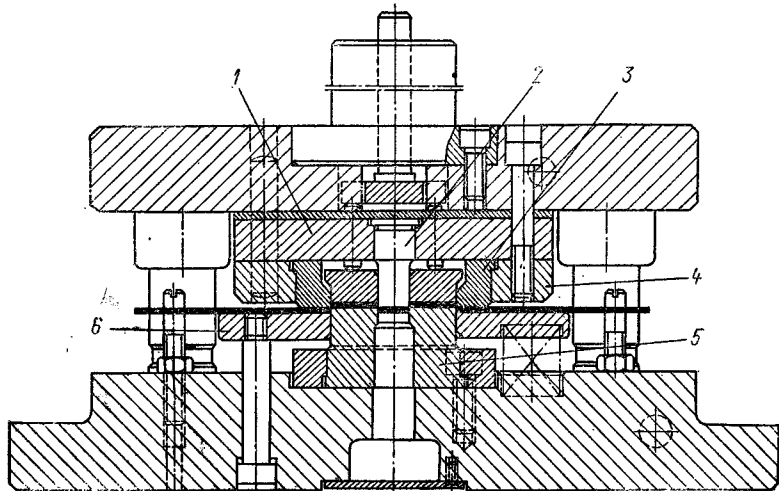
Типовая конструкция штампа совмещенного действия для изготовления кольцевых деталей
